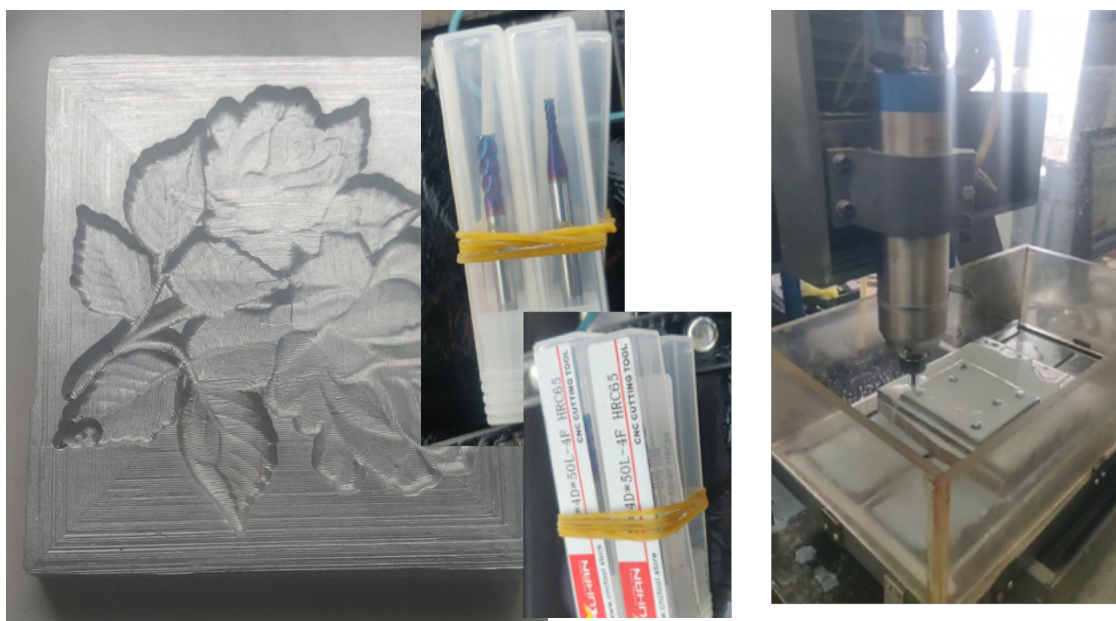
Станок осевой фрезерный с ЧПУ по металлу и изготовленная матрица из дюралюминия Д16Т $100 \times 100 \times 10$ мм, фрезы концевые твердосплавные 65 HRC
